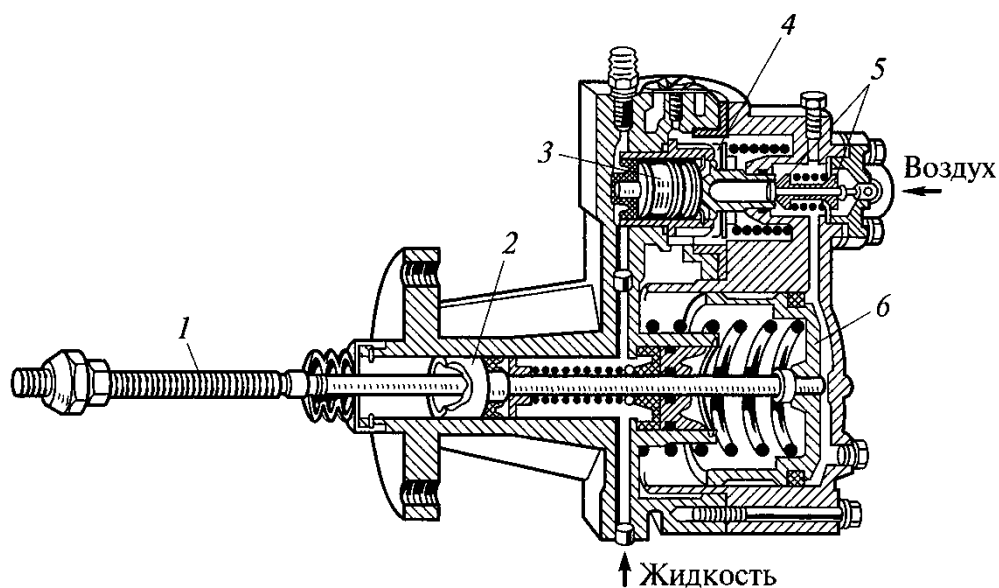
Пневматический усилитель привода сцепления грузовых автомобилей КамАЗ:
